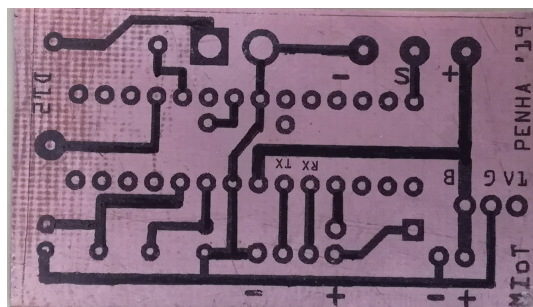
Impressão da PCB do dispositivo sensor em placa de cobre.
